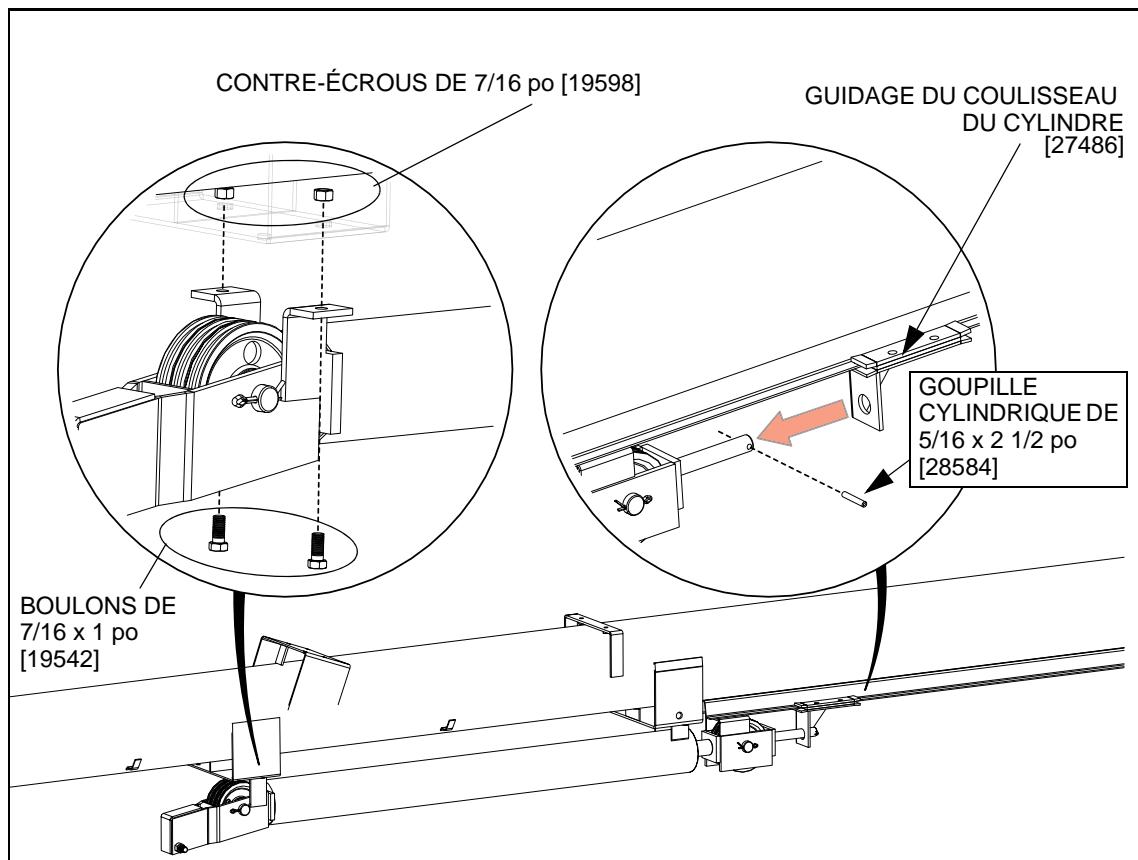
Installation du cylindre de levage (MKX100-83)
